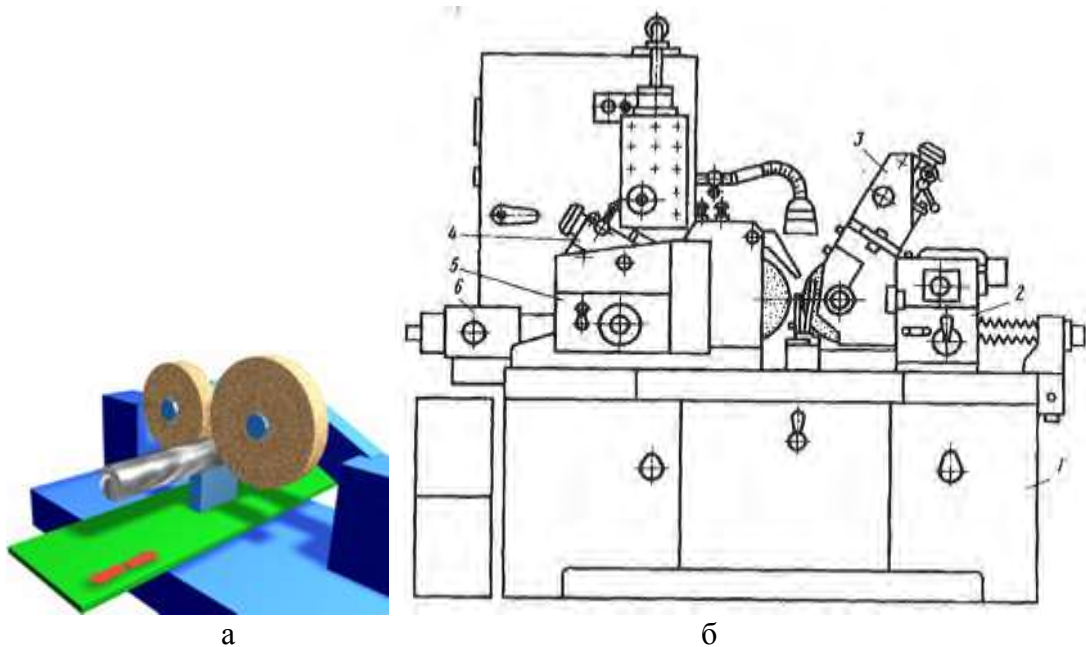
Схема базирования заготовки и общий вид станка 3М184
